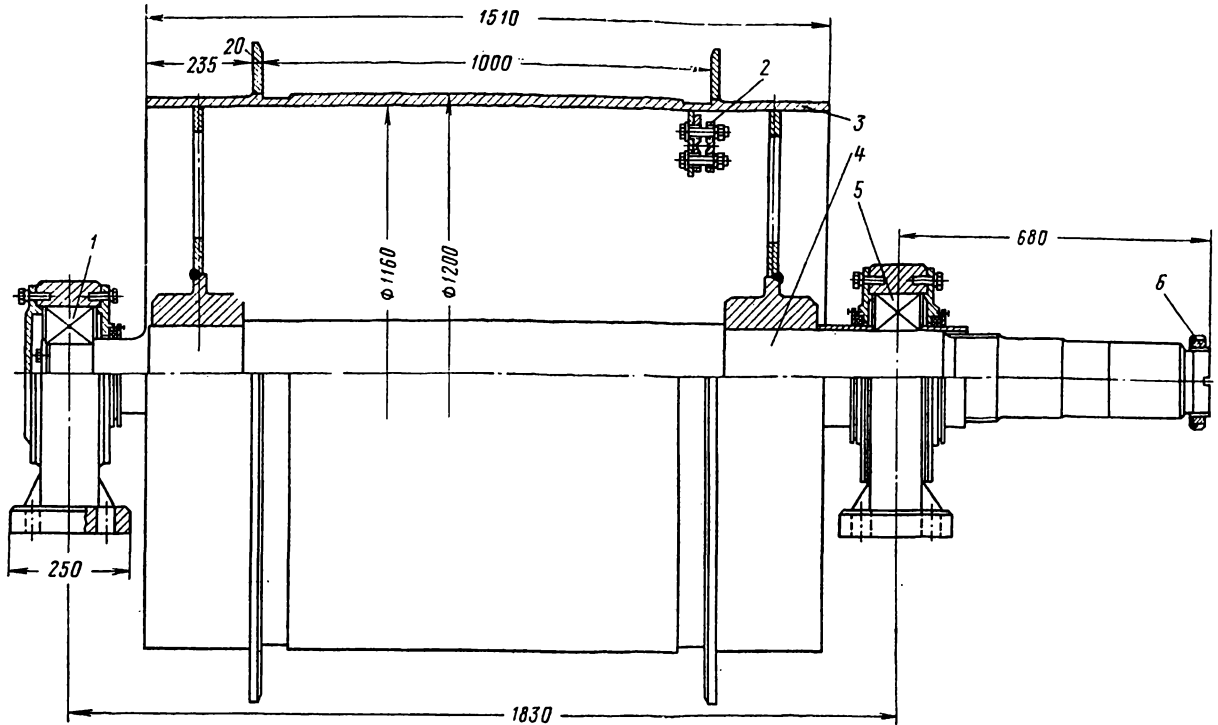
Сборка главного вала машины Ц-1,2×1:
